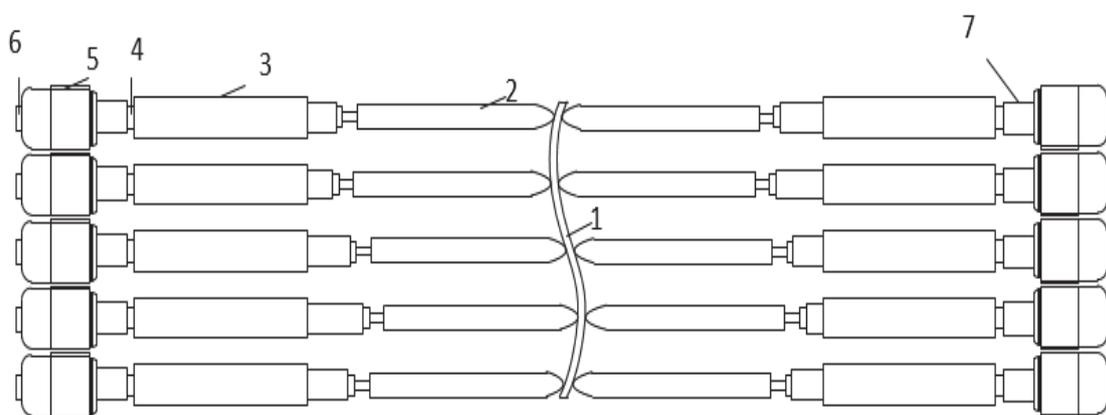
Схематичное расположение формирующих стержней: 1 – заготовка; 2 – стержень; 3 – актуатор; 4 – датчик положения; 5 – двигатель; 6 – датчик скорости; 7 – редуктор
